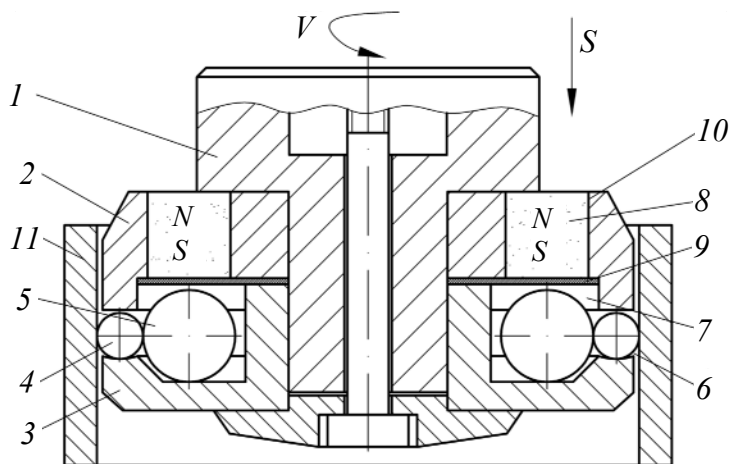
Магнитно-динамический раскатник для упрочняющей обработки внутренней поверхности втулок
